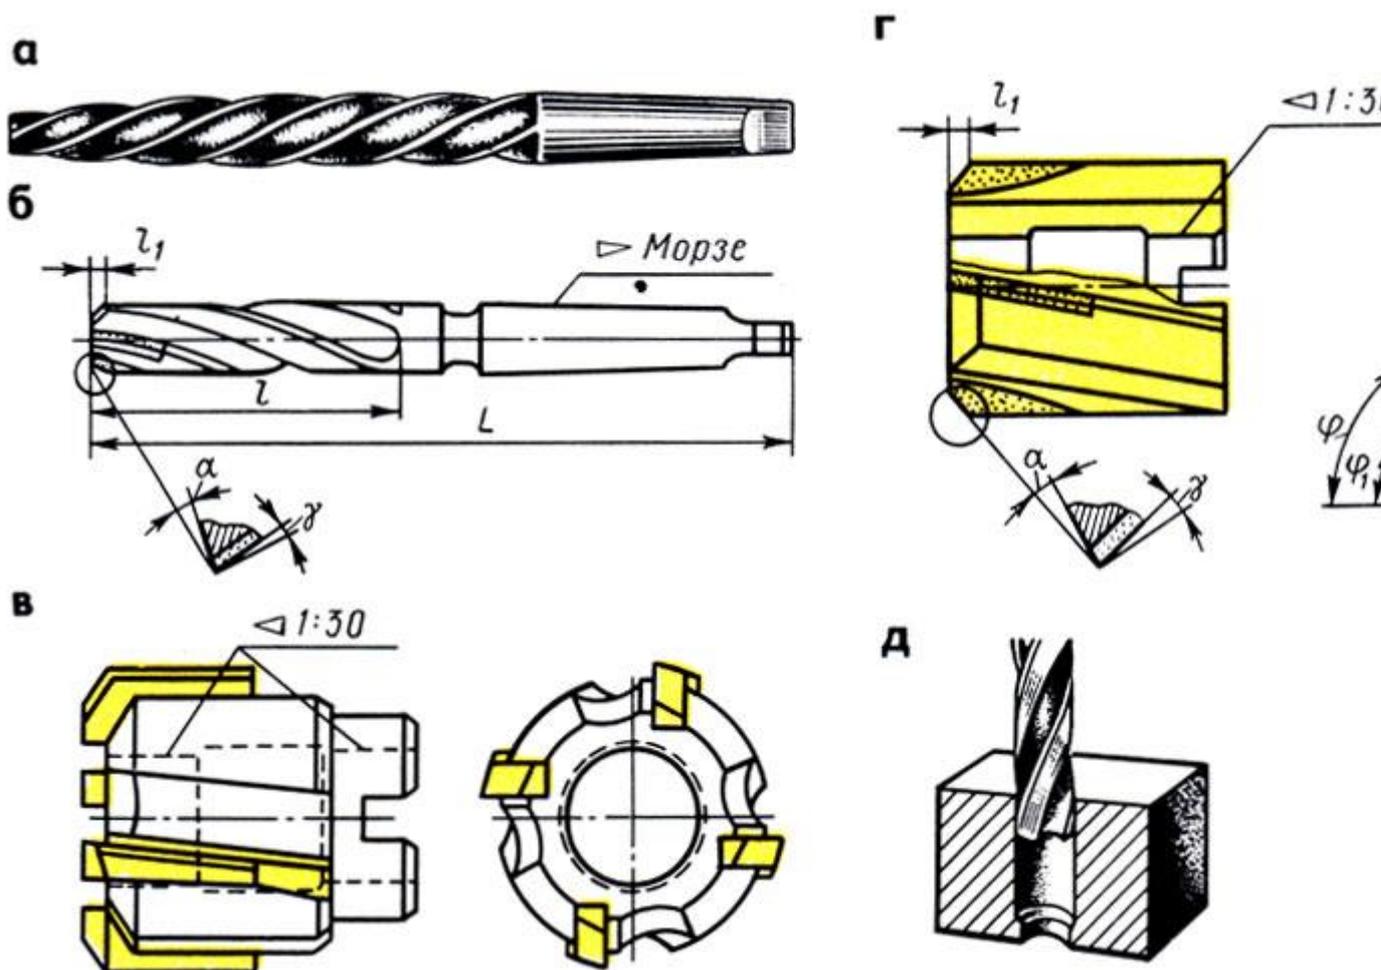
Зенкеры: а - цельный с коническим хвостовиком, б - хвостовой с напаянными пластинками из твердого сплава, в - насадкой со вставными ножами, г - насадной с напаянными пластинками, д - работа зенкером
